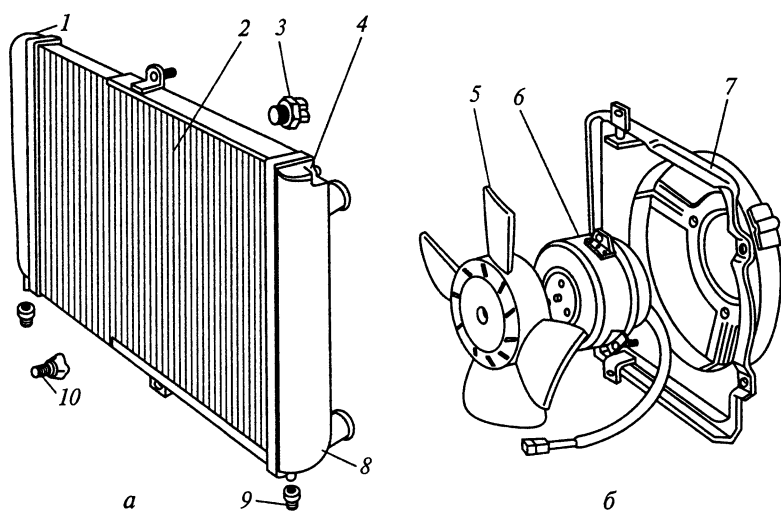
Разборный радиатор (а) и электровентилятор (б) двигателя: 1, 8 — бачки; 2 — сердцевина; 3 — датчик; 4 — прокладка; 5 — вентилятор; 6 — электродвигатель; 7 — кожух; 9 — опора; 10 — пробка
